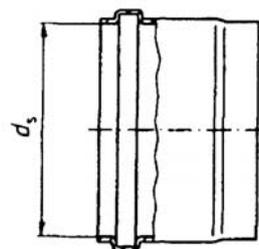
Надвижная муфта для сварки встык концов труб
